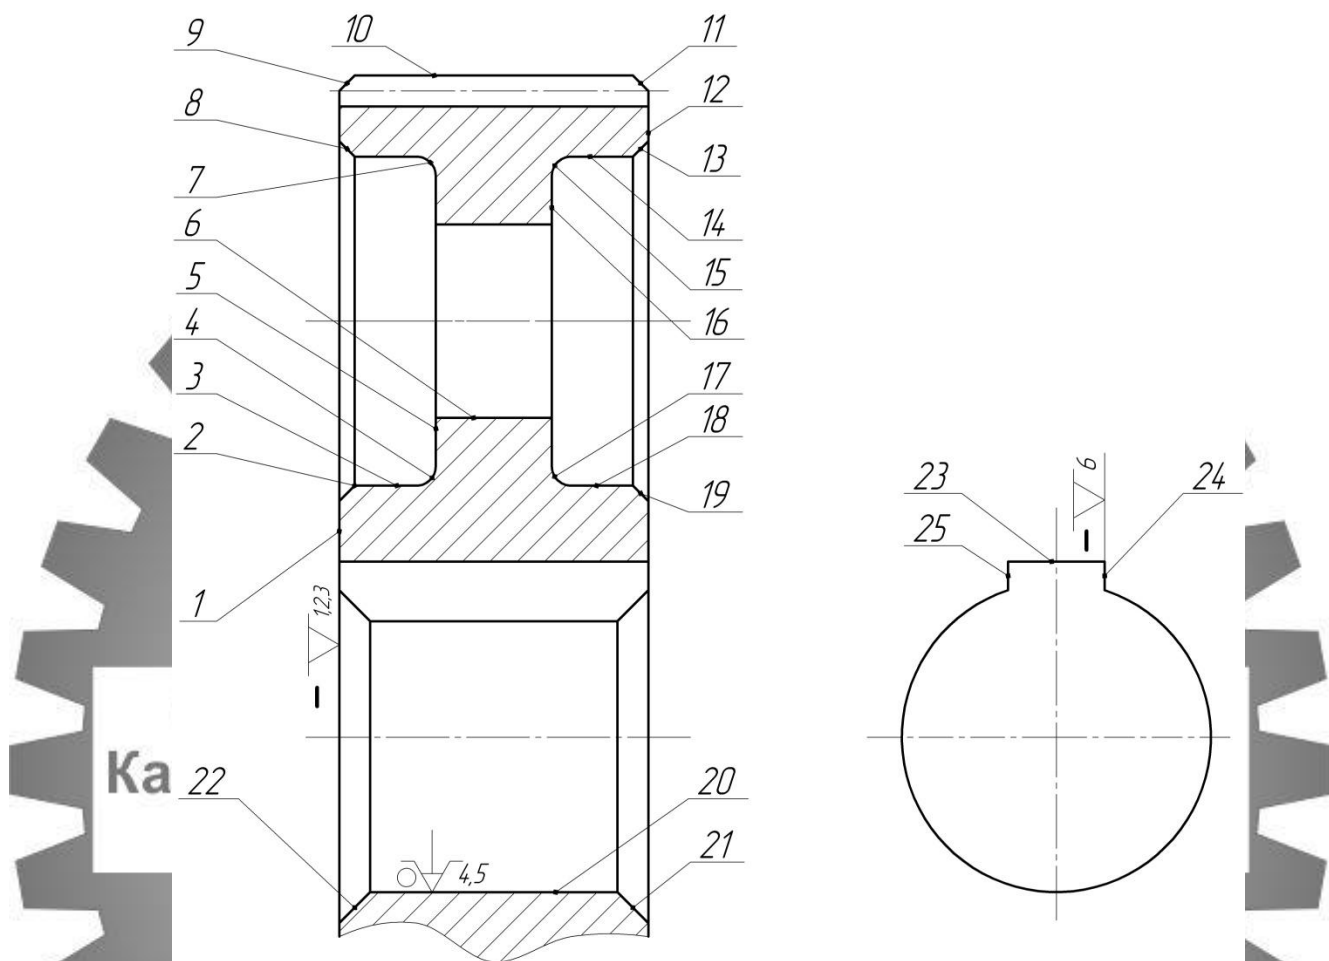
Нумерація поверхонь деталі «Шестерня»
